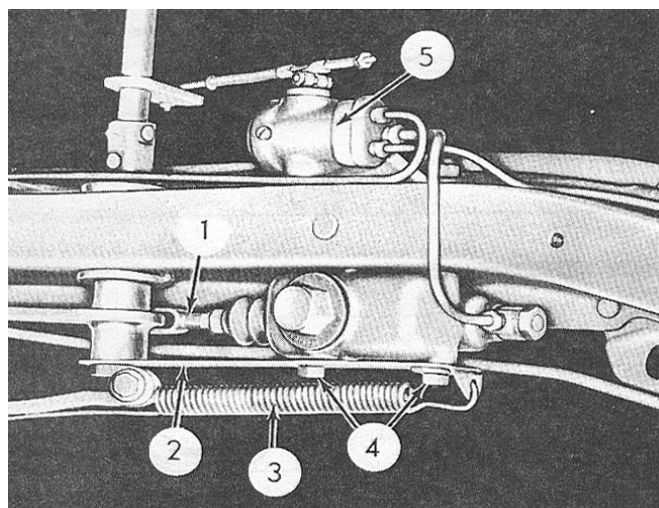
Месторасположение крепления механизма Hill Holder: 1 – шток главного цилиндра; 2 – опорная плита; 3 – педаль сцепления пружинная; 4 – болты крепления цилиндра; 5 – механизм Hill Holder
